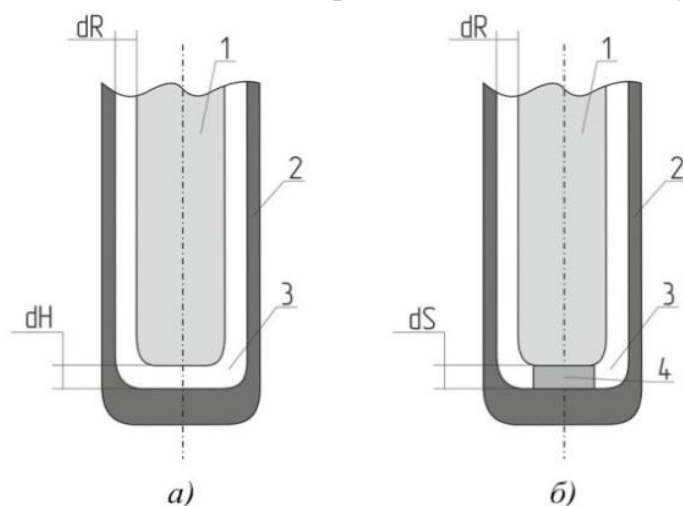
Схема размещения чувствительного элемента в защитной гильзе: а – установка с зазором; б – установка пайкой, 1 – чувствительный элемент ТЭП, 2 – защитная гильза, 3 – свободное пространство, 4 – сварной шов
